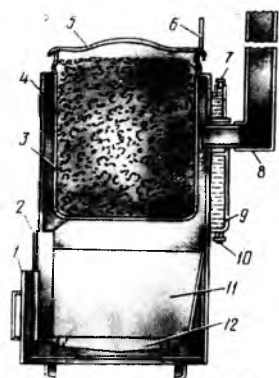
Котел кормоварочный КВТ-60 (в разрезе): 1 — дверца топки; 2 — основание котла; 3 — кормовой бак; 4 — кожух; 5 — крышка; 6 — ручка; 7 — пробка; 8 — труба; 9 — бачок водяной; 10 — кран спускной; 11 — топка; 12 — колосник
